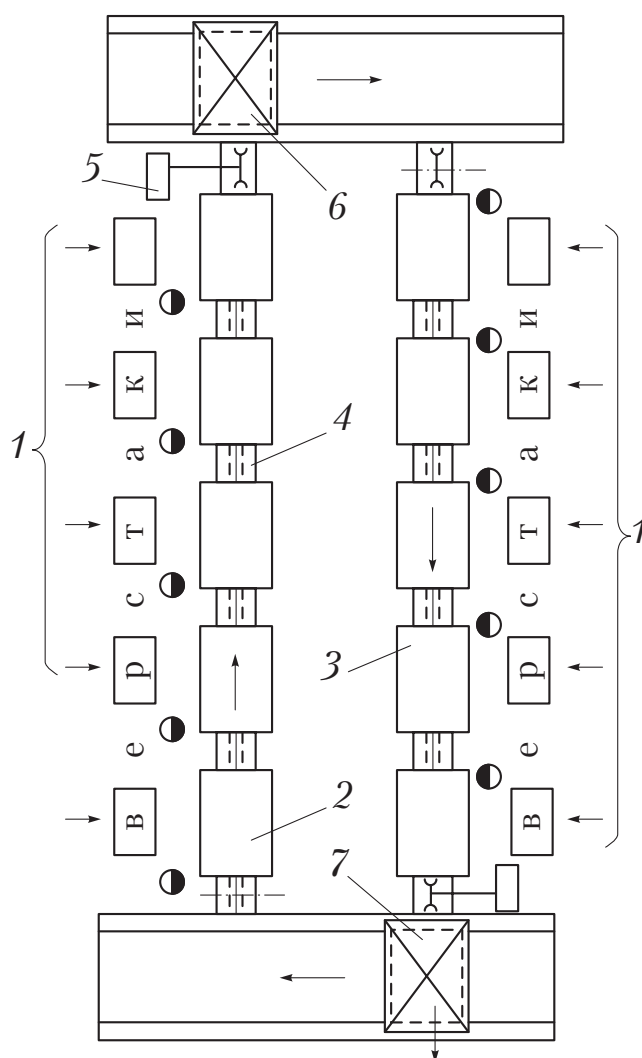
Схема планировки сборочного участка на подвижных тележках: 1 — зона подачи деталей и узлов; 2 — начало сборки; 3 — тележка; 4 — цепь конвейера; 5 — привод конвейера; 6 — передача объекта на другую ветвь конвейера; 7 — выдача собранного изделия
